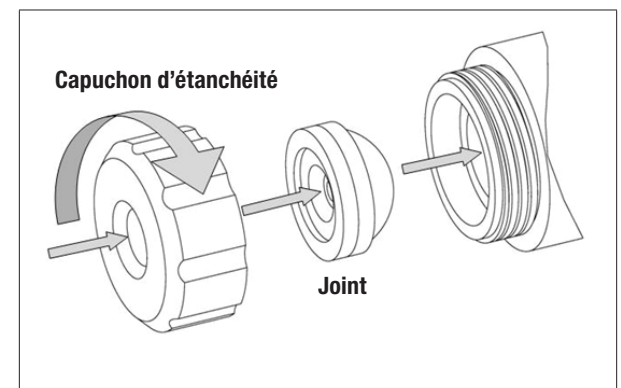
INSTALLATION DU JOINT D'ÉTANCHÉITÉ
